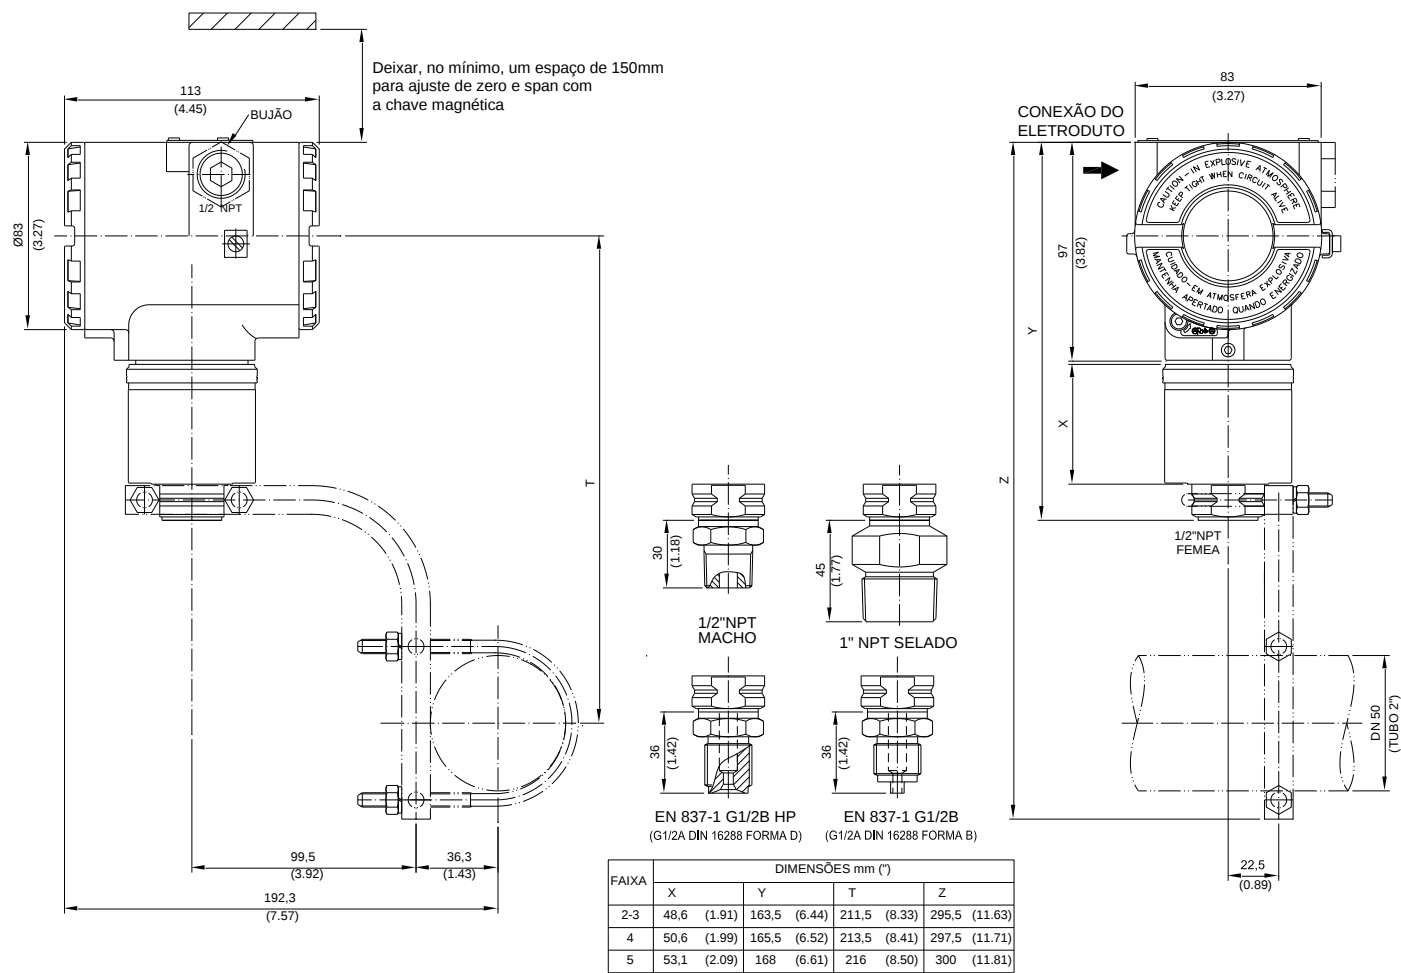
(a) – Desenho Dimensional e Posição de Montagem para o LD293 – Transmissor com Suporte de Montagem
